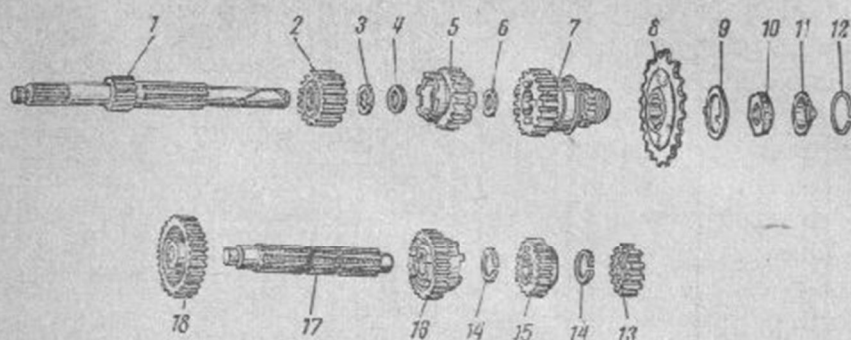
Детали коробки передач (позиции даны в табл. 28)
